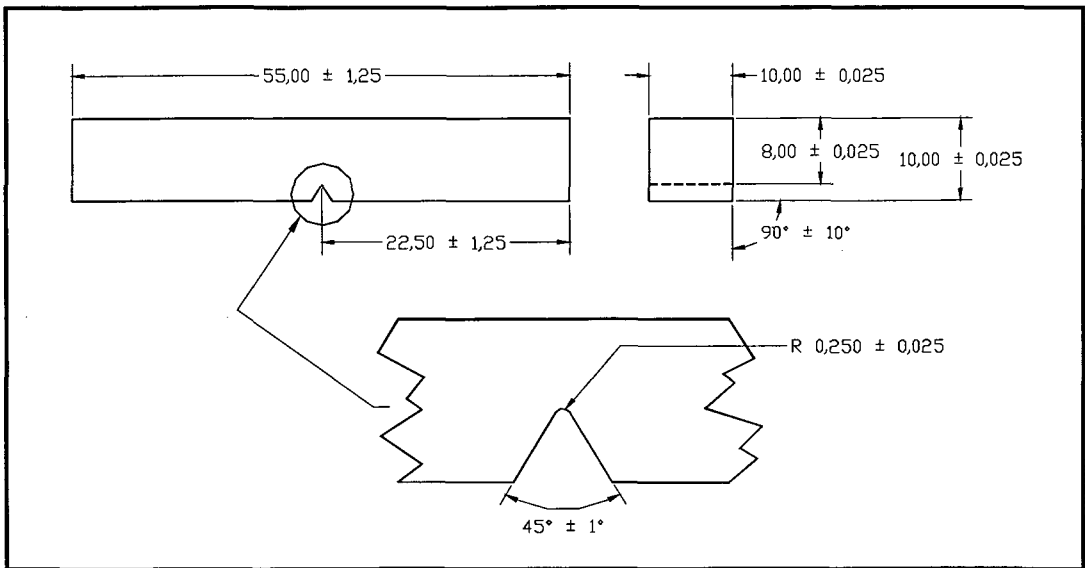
Detalhe do corpo de prova de resistência ao impacto charpy-V. Dimensões em mm.
